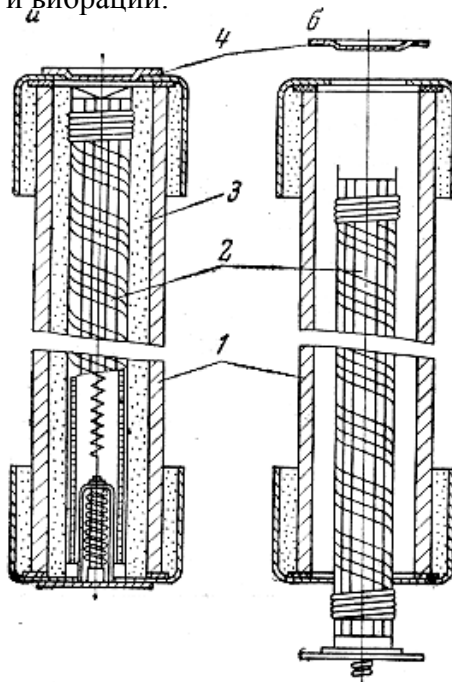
Предохранитель ПКЭ-6: а – заряженный; б – при сборке или разборке; 1 – патрон (фарфоровая трубка); 2 – плавкая вставка; 3 – кварцевый песок; 4 – латунные колпачки.
